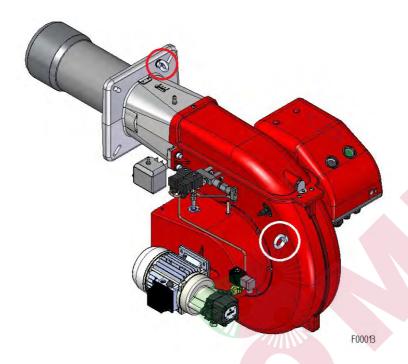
Транспортировочные рым-болты FGP 75/M - 100/М EVO
